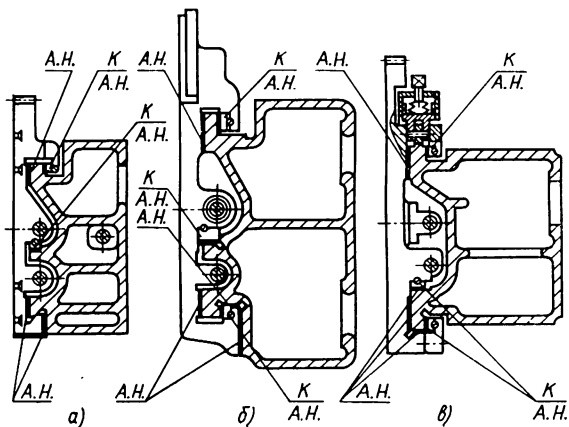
Схемы направляющих скольжения салазок суппортов:
